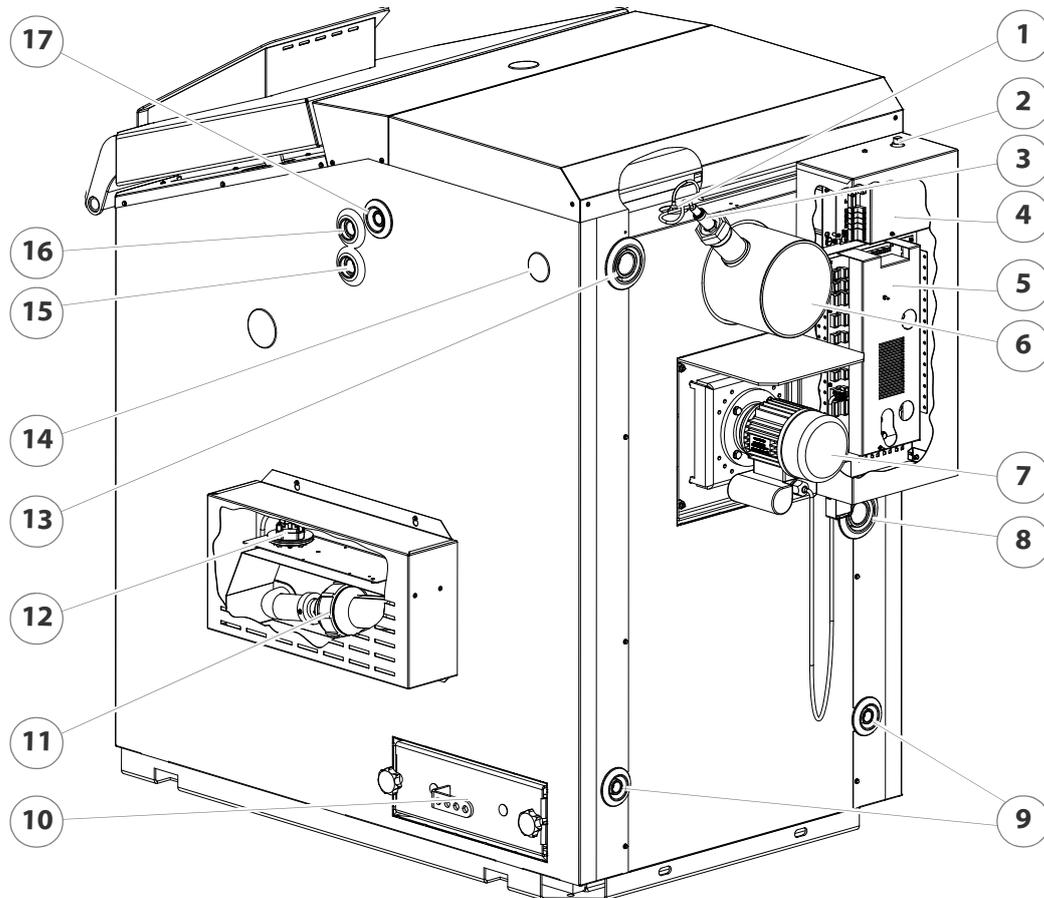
/3 - Vue arrière et latérale HDG Euro 30/40/50
